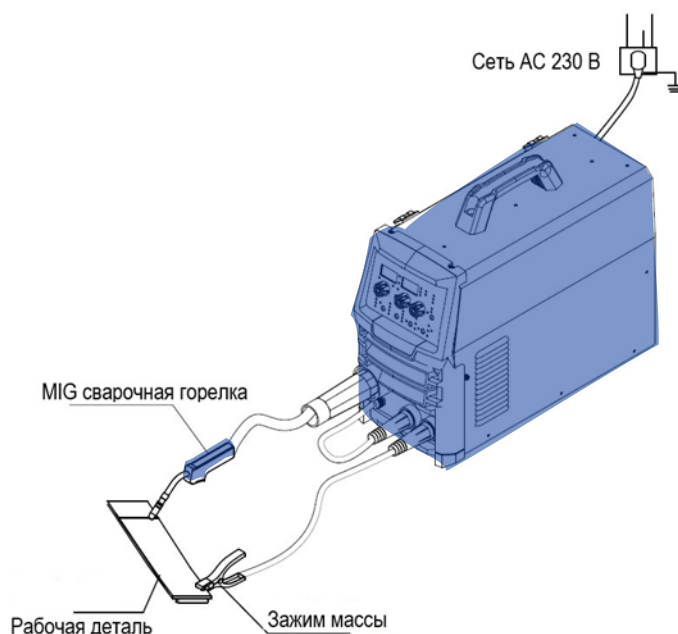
Схема подключения в режиме FCAW (сварка порошковой проволокой NO GAS)
